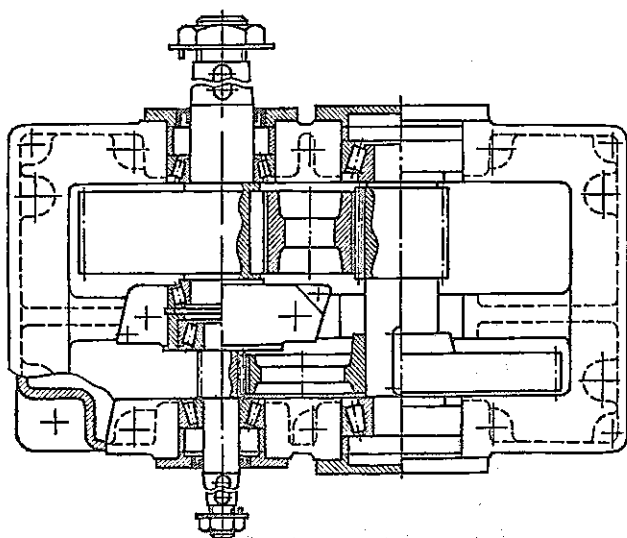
Двухступенчатый редуктор с соосными валами
